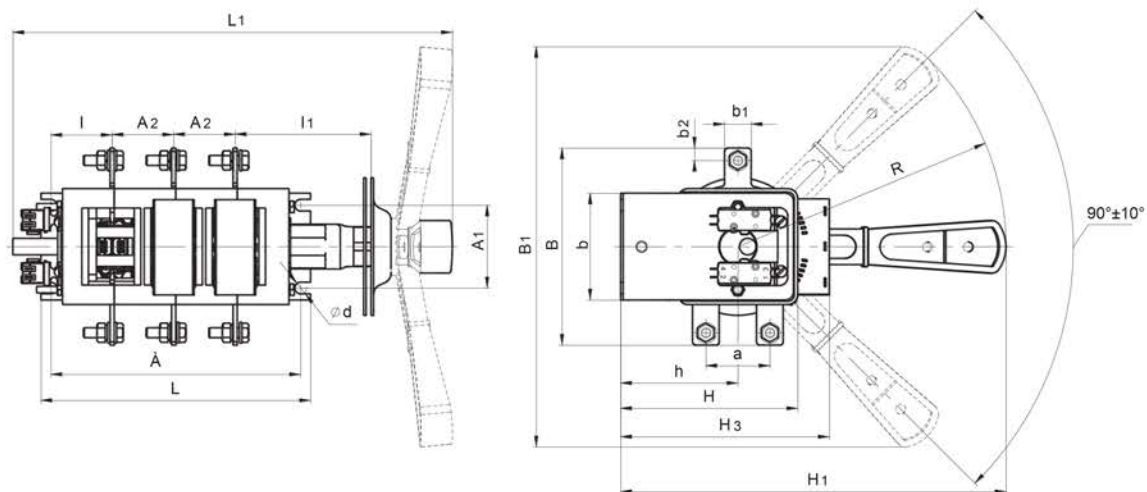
Выключатель-разъединитель трехполюсный на два направления с боковой несъемной рукояткой.
